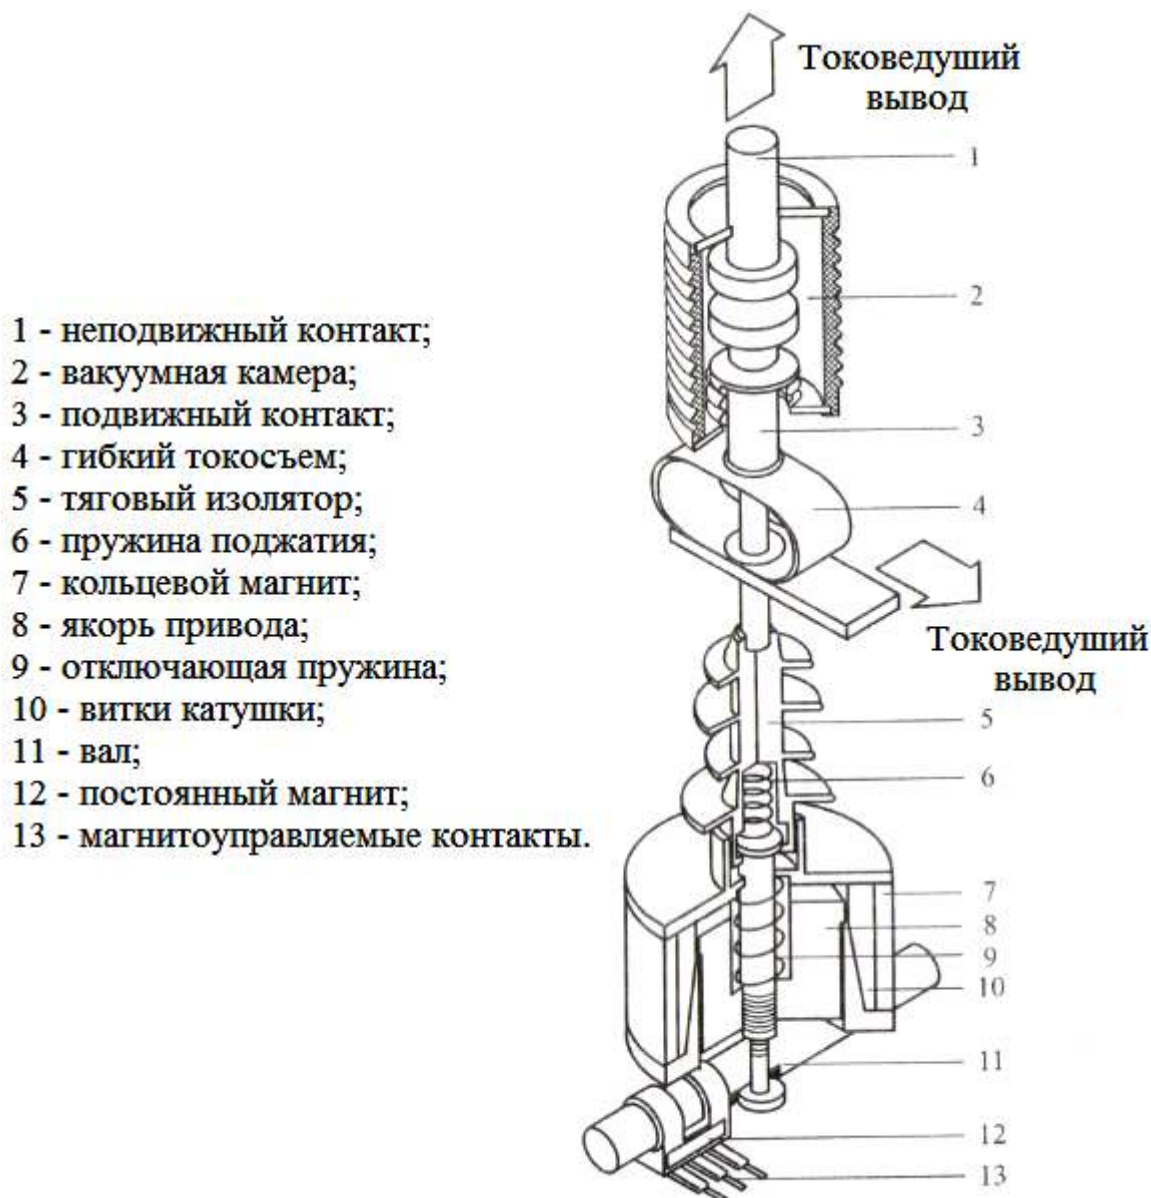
Устройство полюса выключателя ВВ/TEL-10-12,5/1000 У2
